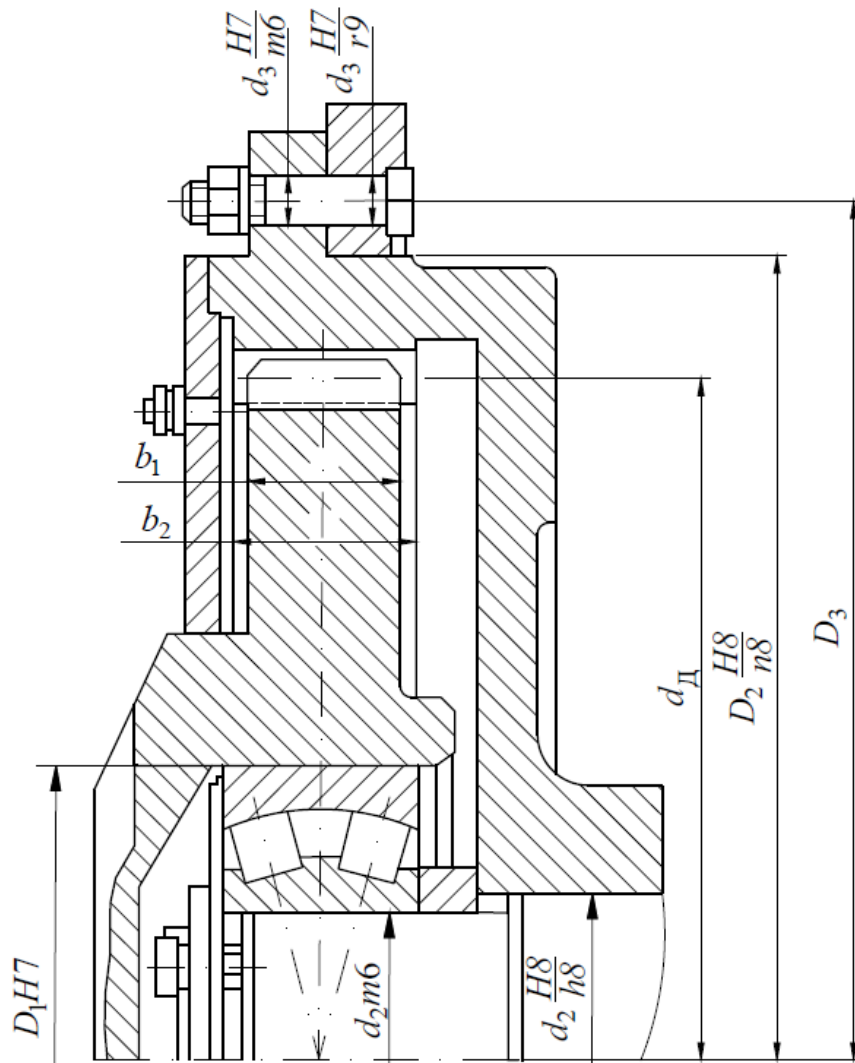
Зубчатые муфты для соединения редукторов с барабанами
